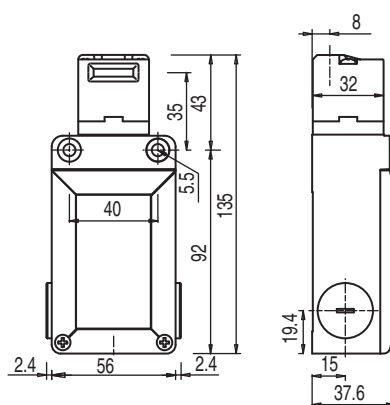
Dimensiones de L100-P3C3-M20-MLM24 en mm
